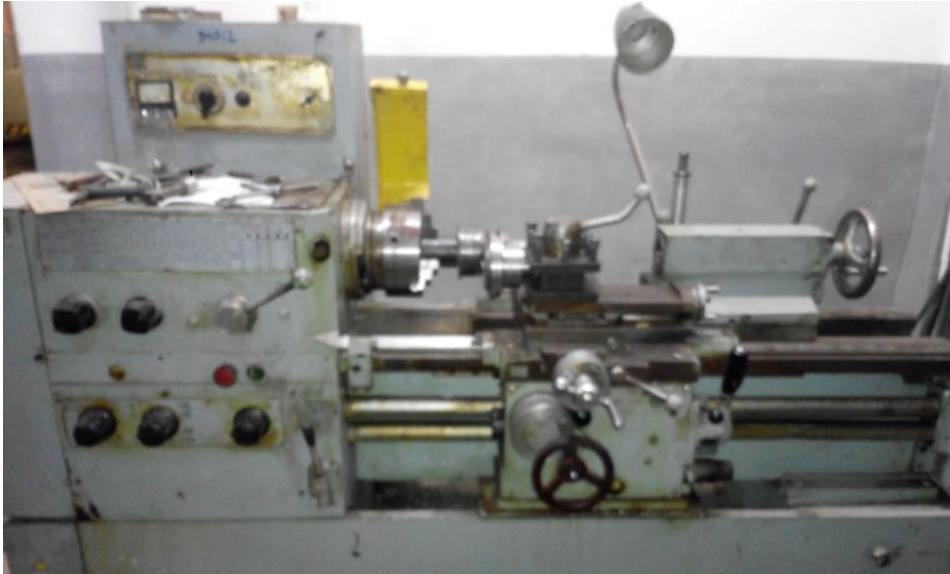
Загальний вигляд верстата із закріпленим приспособленням
